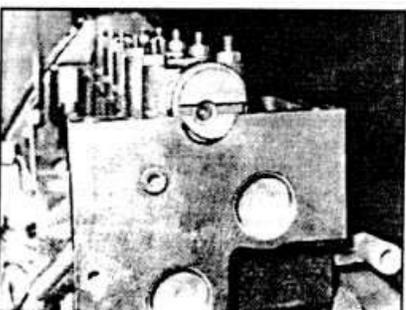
Е.25. Расположение паза распределительного вала при установке головки блока цилиндров.
